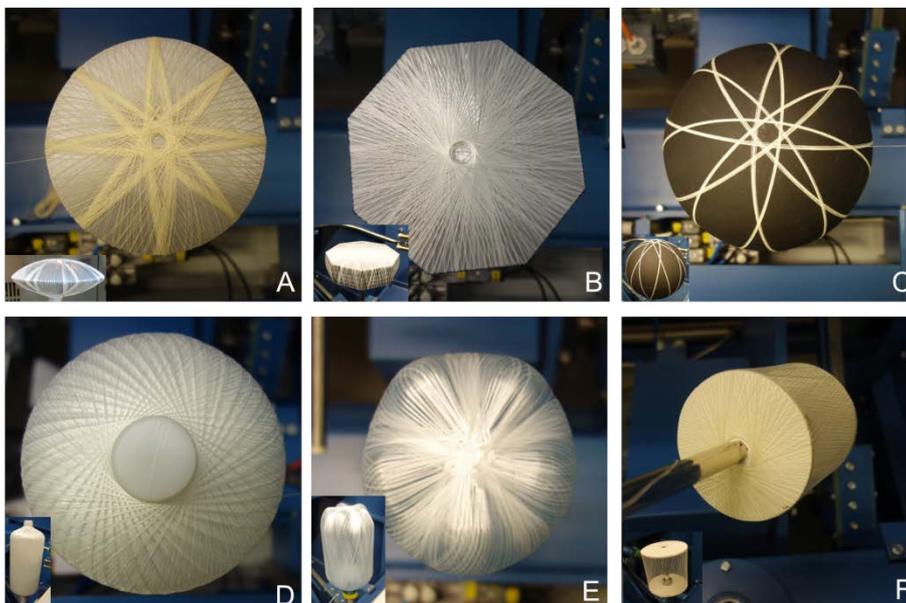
Beispiele für umknäuelte Formen: A) Linsenform, B) achteckiges Prisma, C) Kugel, D) typische Druckbehälterform, E) PET-Hohlkörper, F) Zylinder
